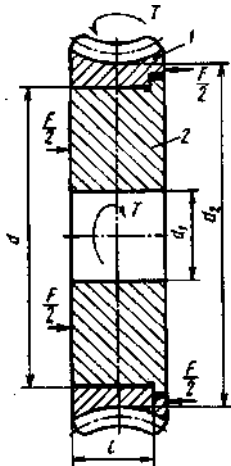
Соединение с натягом венца червячного колеса с центром;
